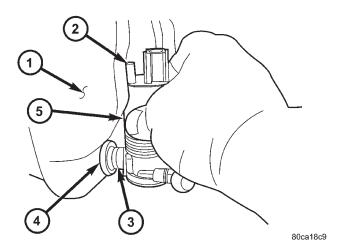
Desmontaje e instalación de bomba y motor del lavador
